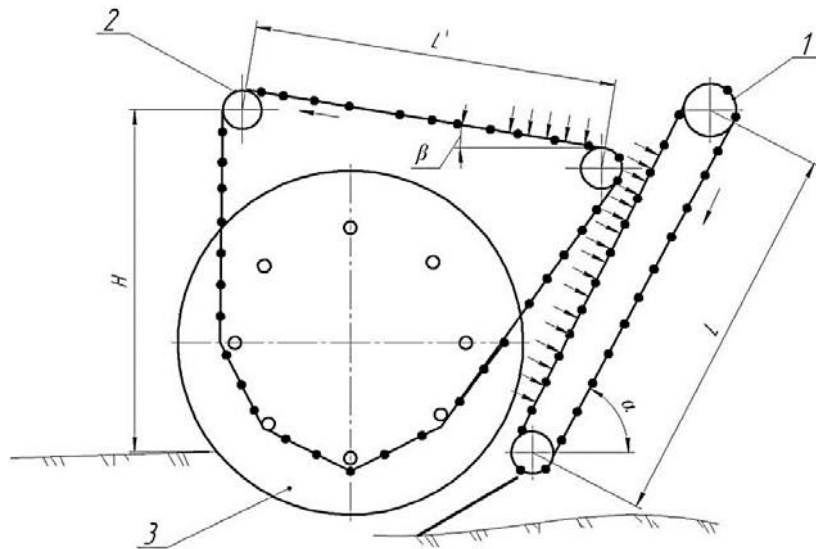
Схема до визначення опору руху елеваторного полотна: 1 – ворохо-підйомний елеватор; 2 – клубне-приймальний елеватор; 3 – диск.
